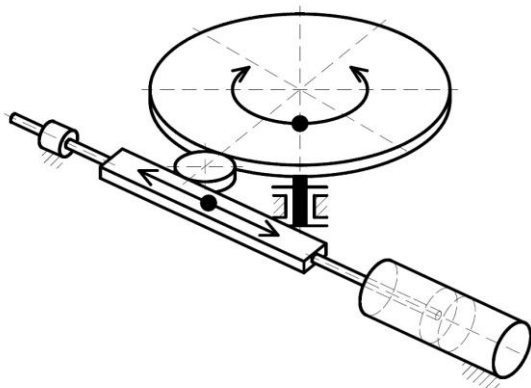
Rotační motor – kývný pohyb1 [2]
